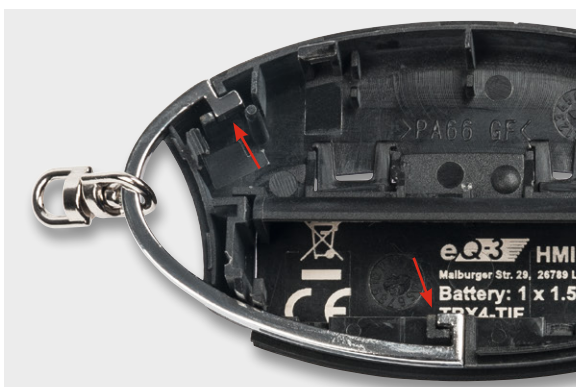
So wird der Metallbügel in die Gehäuseunterschale gelegt.
